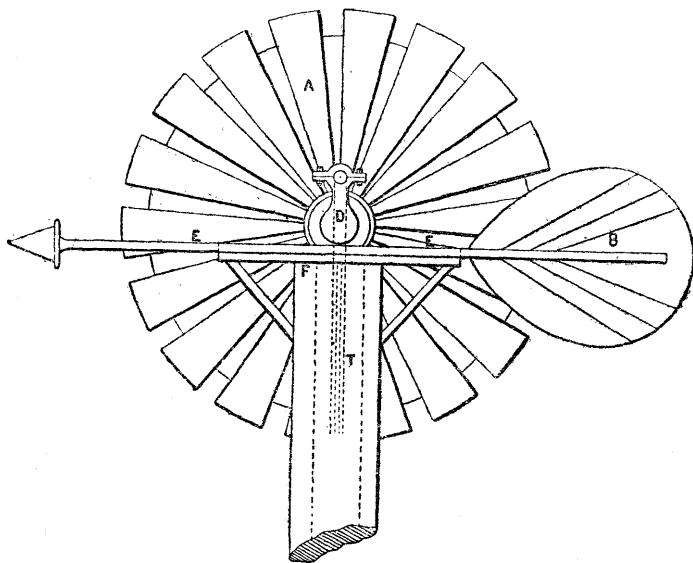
Moulin Fustin*. Vue d'arrière.
